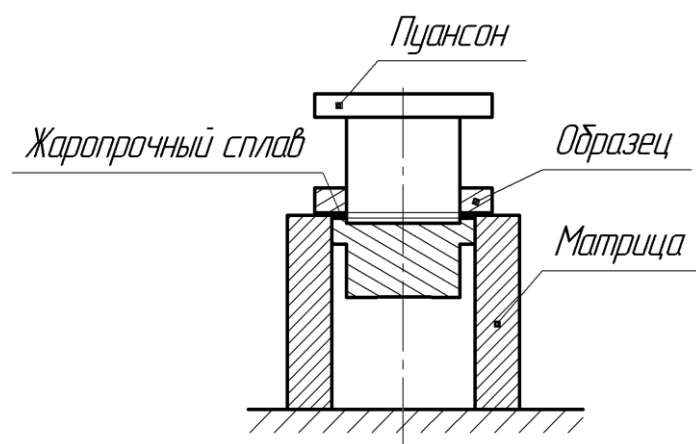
Схема испытания триметаллического образца на отрыв плакирующего слоя
